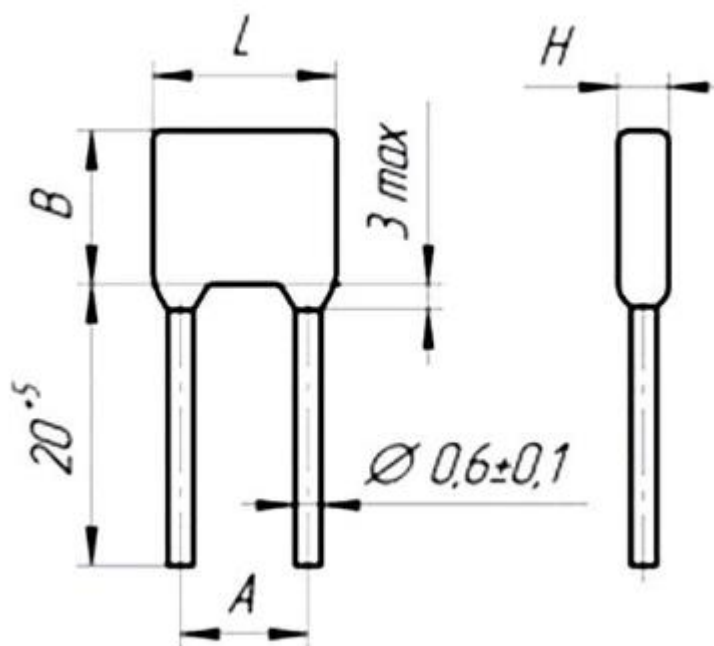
Габаритні розміри керамічного конденсатора
